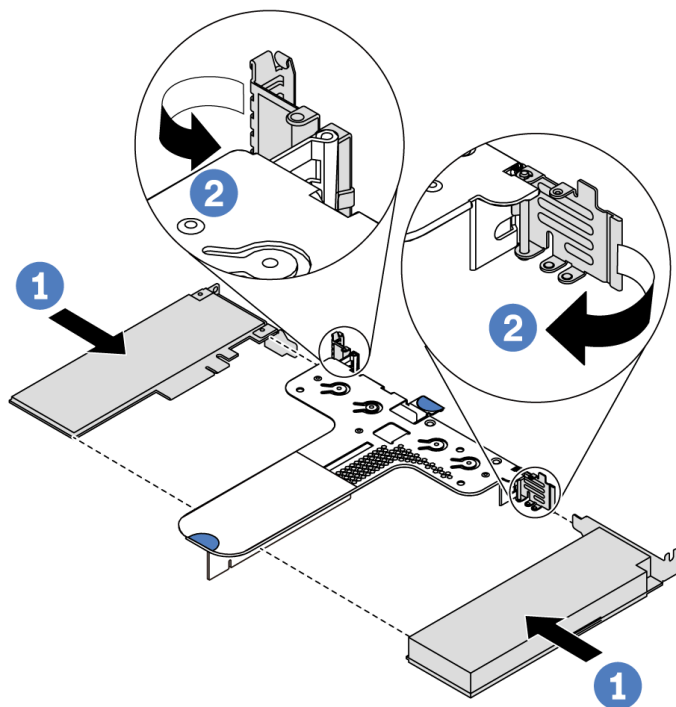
Instalação do conjunto de placa riser 2 (LP+LP)
